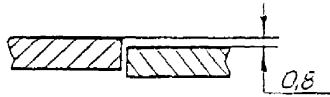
Допустимые смещения кромок при сварке
